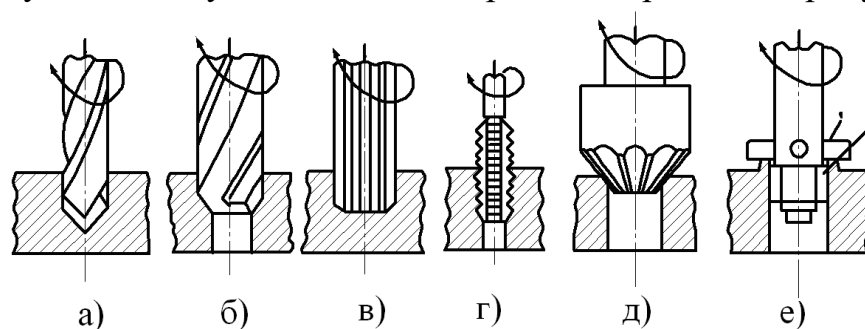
Схеми обробки на свердильному верстаті: а - свердління; б – зенкерування; в - розгортання; г - нарізування різьблення мітчиком; д - зенкування; е – цекування
